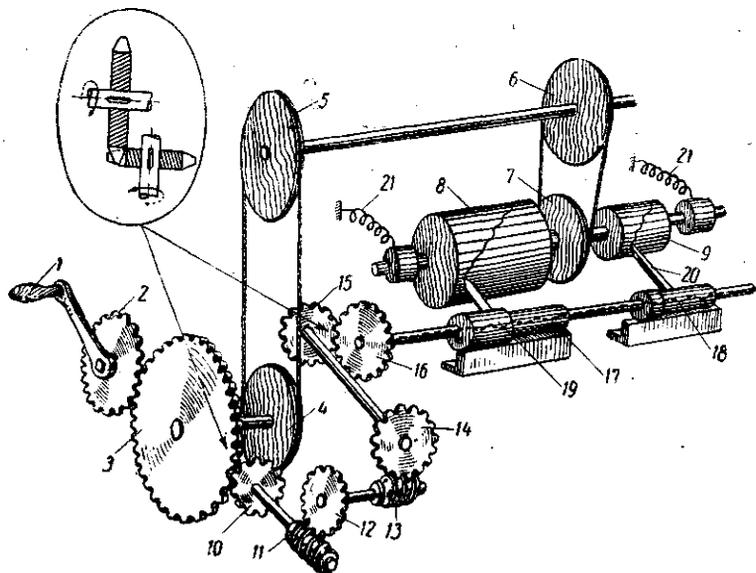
Кинематическая схема большого токарно-контрольного станка Нартова 1718—1729 гг.
